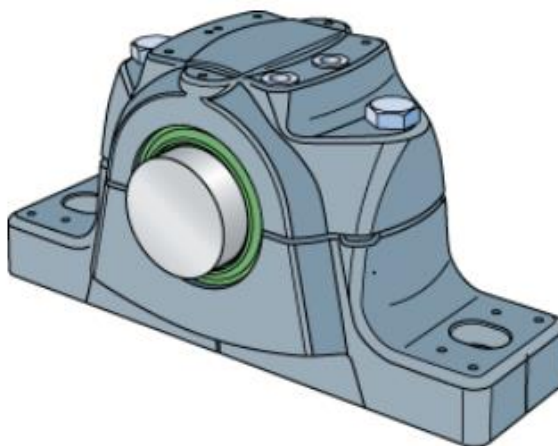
Soudečkové ložisko SKF – řada E [24]
